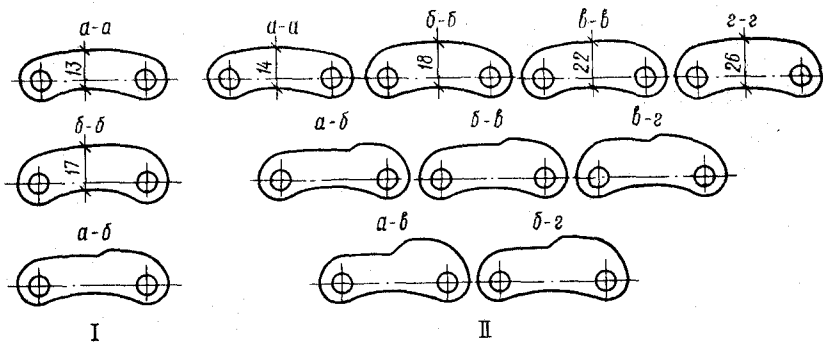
Схема пластин картона для двухуточного прибора (I) и четырехуточного прибора (II) станков СТБ
